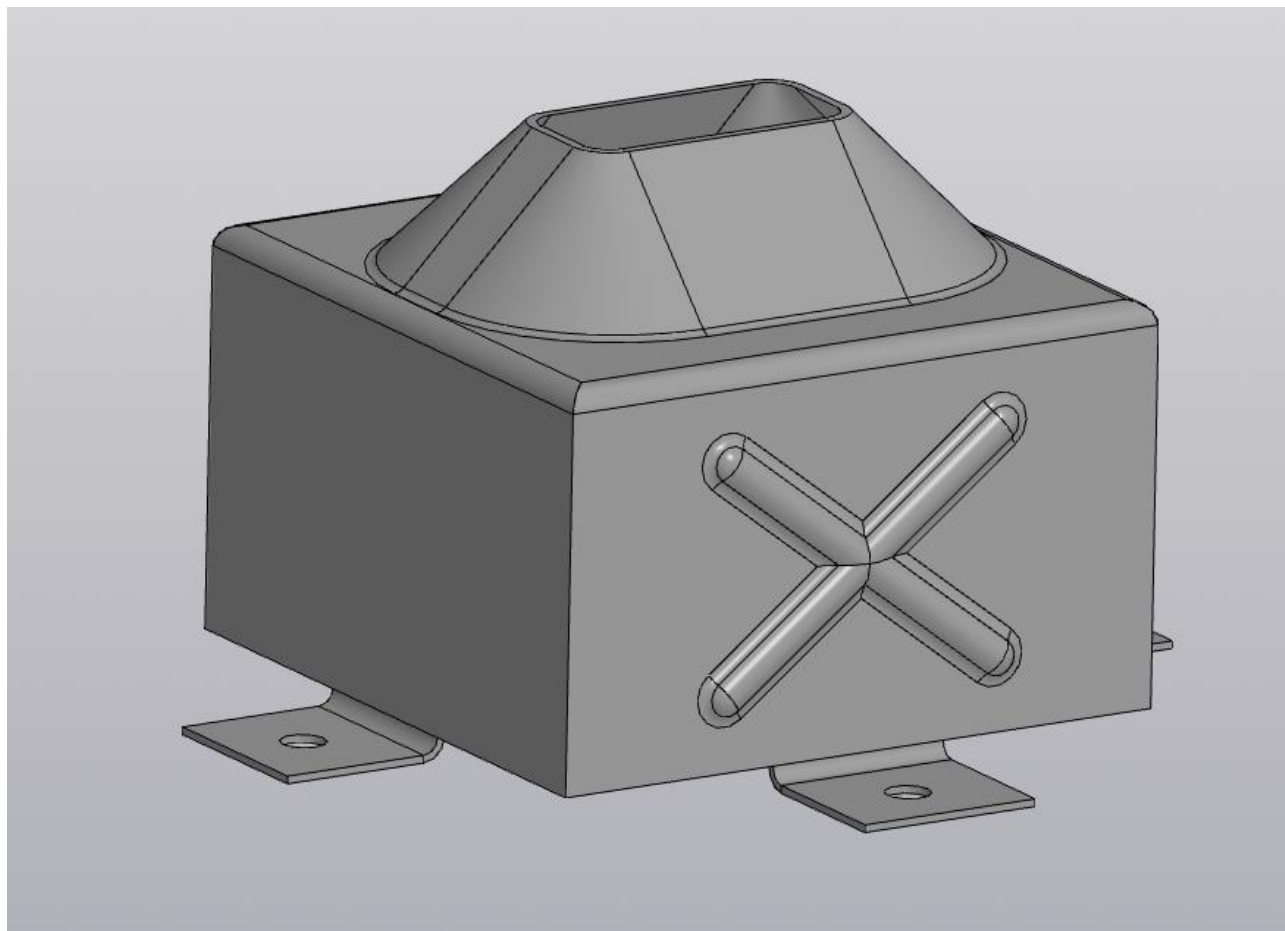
3D-модель детали «Корпус 2» (вариант 3)
